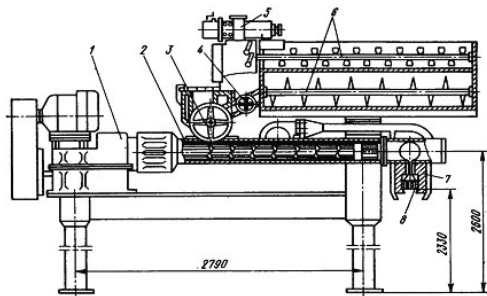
Схема шнекового макаронного процесса ЛПЛ – 2М: 1–привод; 2– два прессующих корпуса; 3– вакуумный тестомеситель; 5–дозировующее устройство; 6–тестомесители; 7–тубус; 8–прямоугольные матрицы
